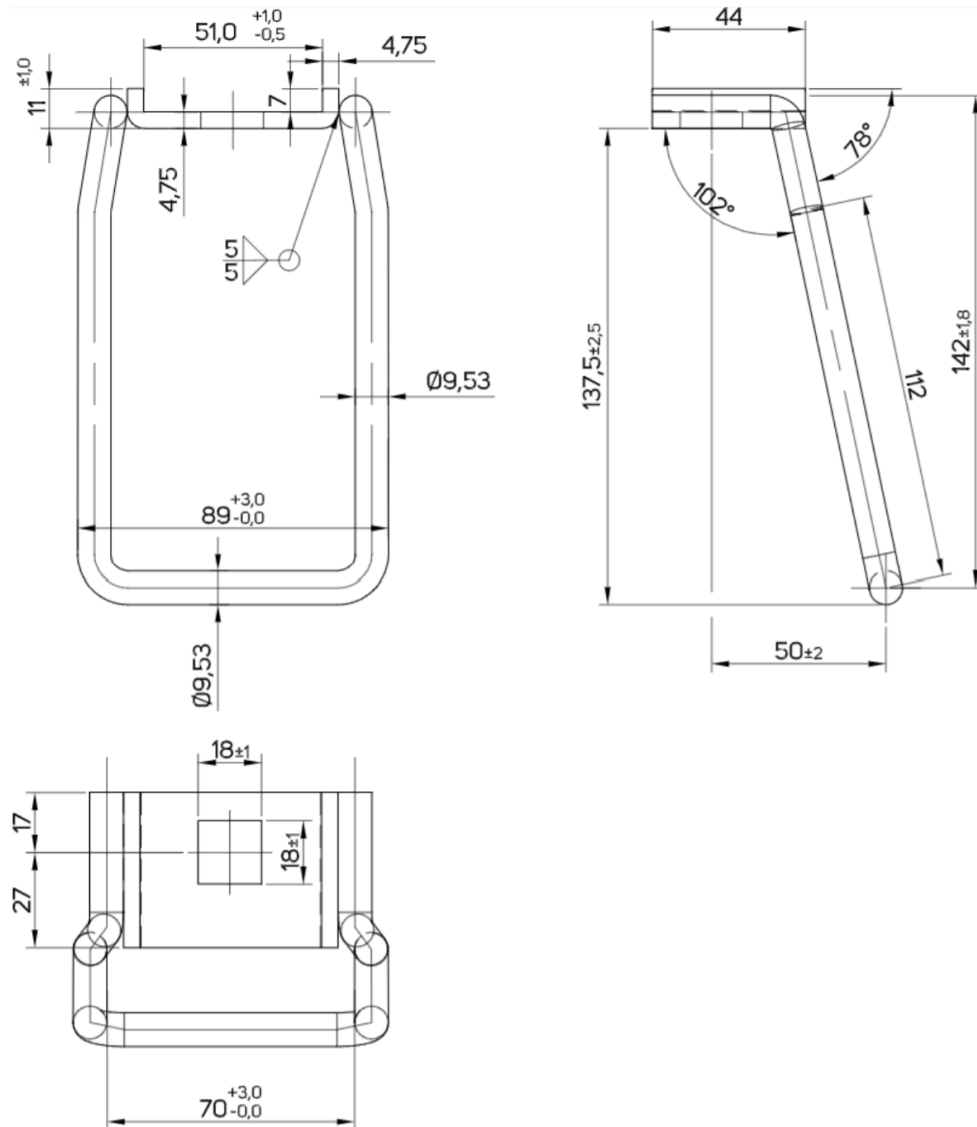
Desenho estribo para braço tipo L (Autor, 2020).
